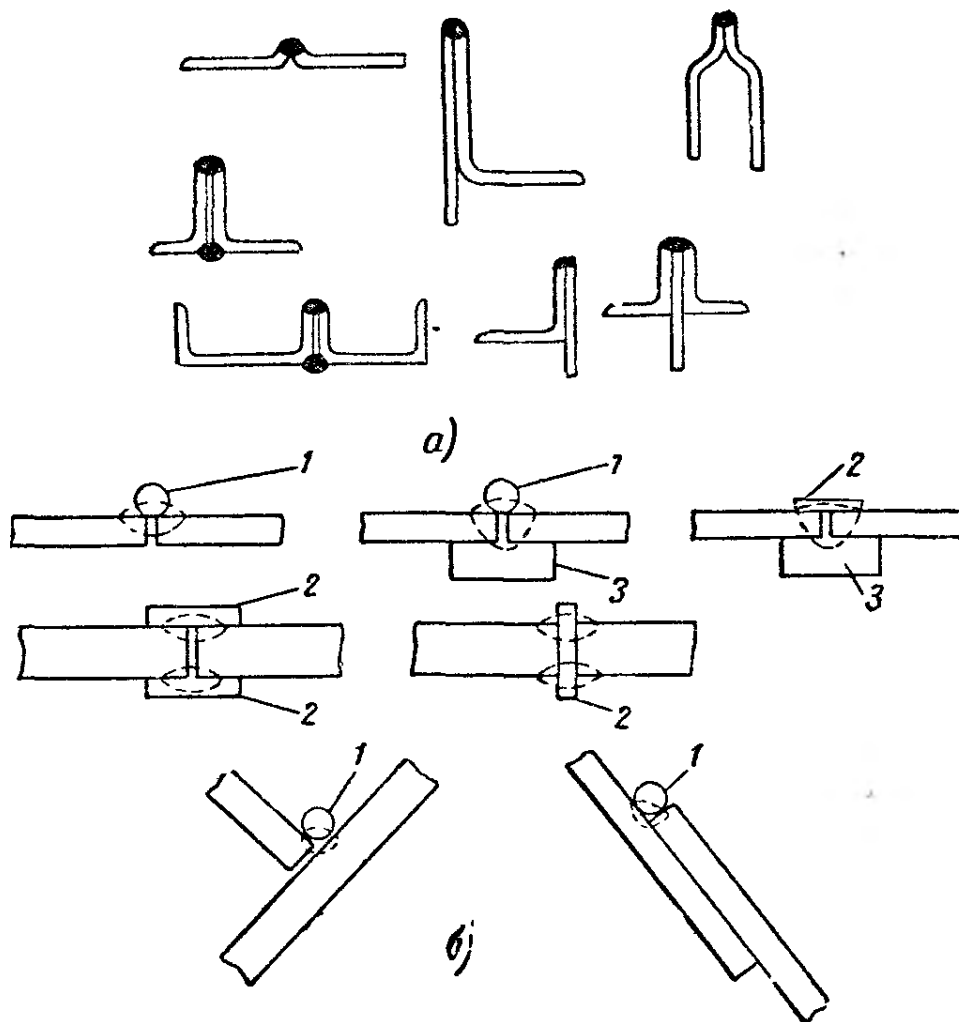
Некоторые виды сварных соединений при сварке угольным электродом:
